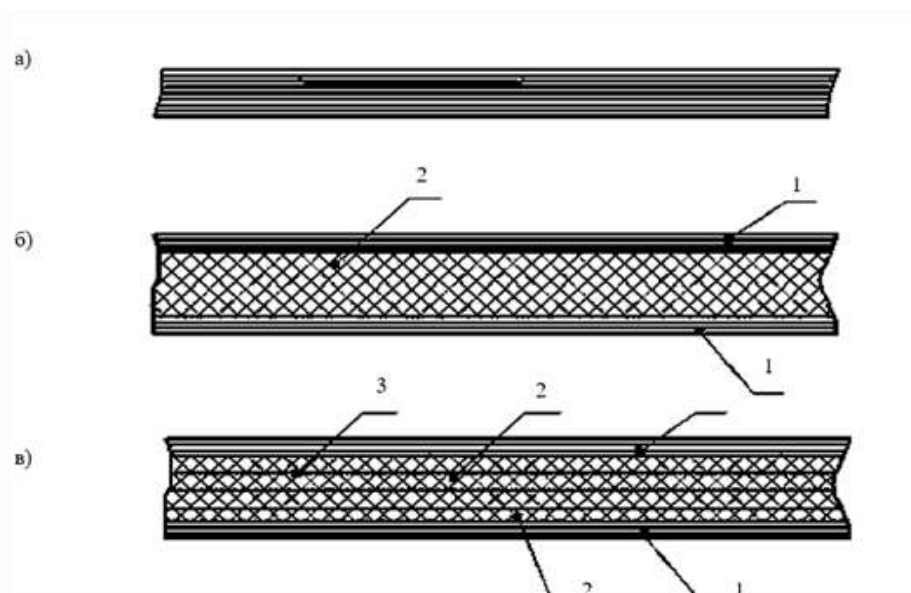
Конструктивні схеми обшивки корпусу (настилів палуб і полотниць перегородок) з ПКМ:
